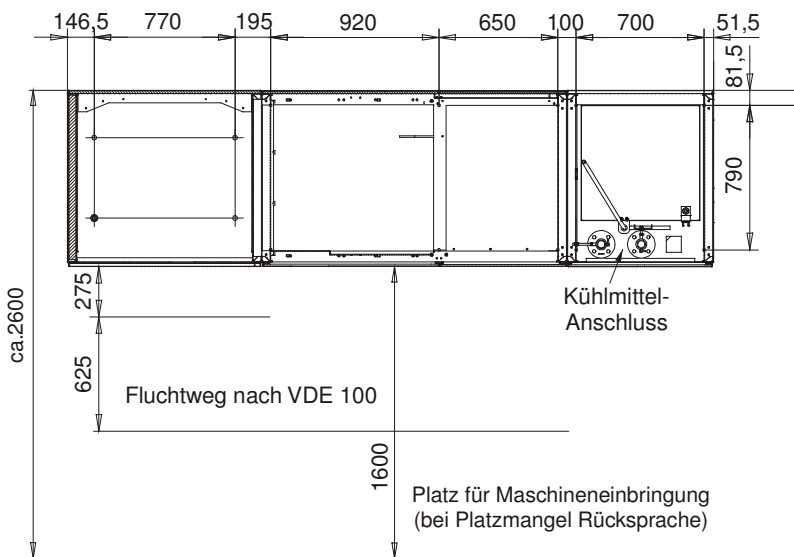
Abmessungen UB420 – UB625 mit Wasserkühlung
